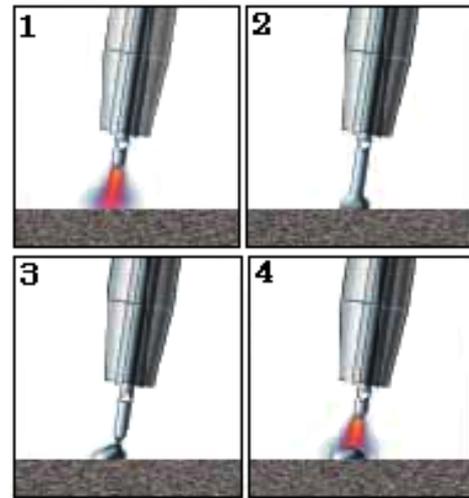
Esquema del proceso de transferencia de metal en la soldadura por transferencia de metal en frío. [10]
